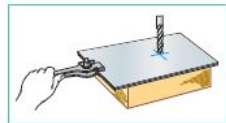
Закрепление заготовки в ручных тисках. Установка подкладной доски
